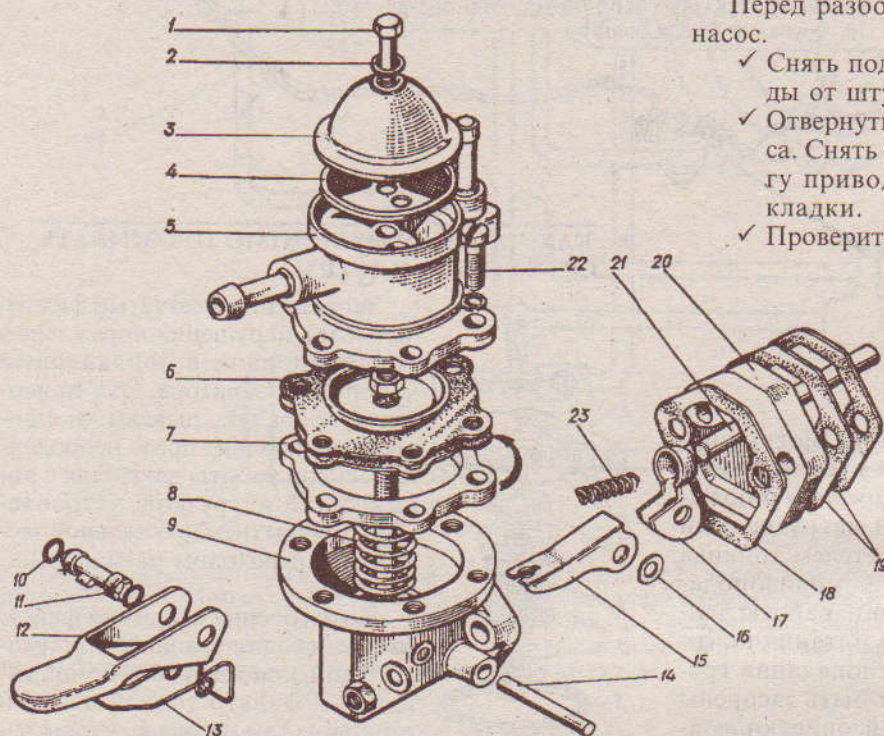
Детали топливного насоса: 1 - болт крышки; 2 - шайба уплотнительная; 3 - крышка; 4 - фильтр; 5 - верхний корпус; 6 - диафрагма насоса в сборе; 7 - дистанционная прокладка; 8 - центральная пружина; 9 - нижний корпус; 10 - кольцо уплотнительное; 11 - эксцентрик; 12 - рычаг; 13 - пружина рычага; 14 - ось рычага и балансира; 15 - балансиры; 16 - шайба рычага заполнителя; 17 - рычаг привода; 18 - прокладка; 19 - прокладки регулировочные; 20 - проставка; 21 - штанга; 22 - винт с пружинной шайбой; 23 - возвратная пружина рычага
